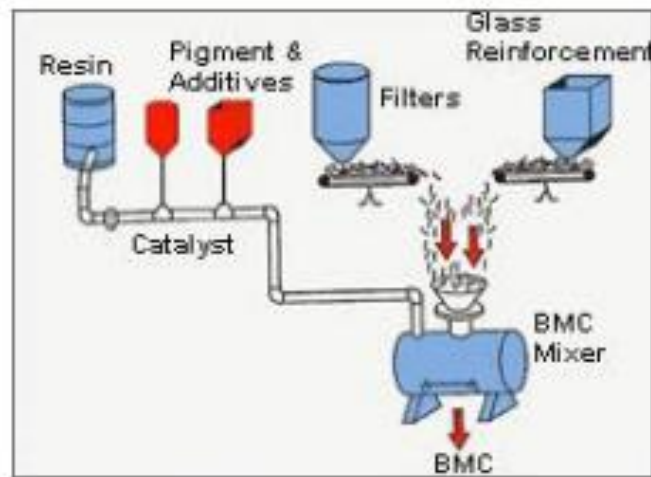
Representación del proceso moldeo por compresión en caliente de un compuesto.²⁰
